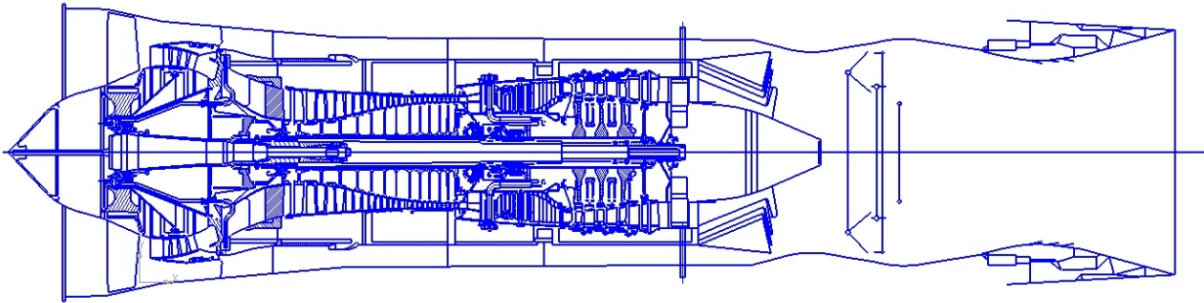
Конструктивно-компоновочная схема ТРДДФ с опорными ступенями КНД
